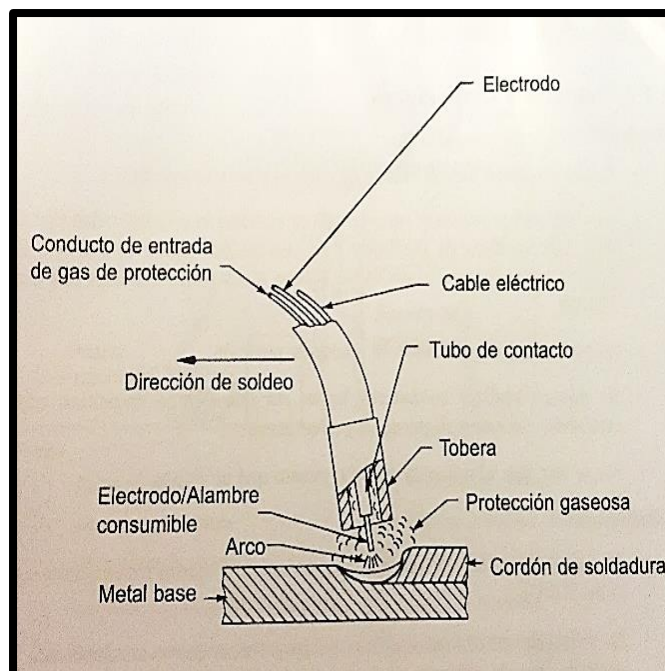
Soldeo por arco con gas. Tomada del Manual del soldador
